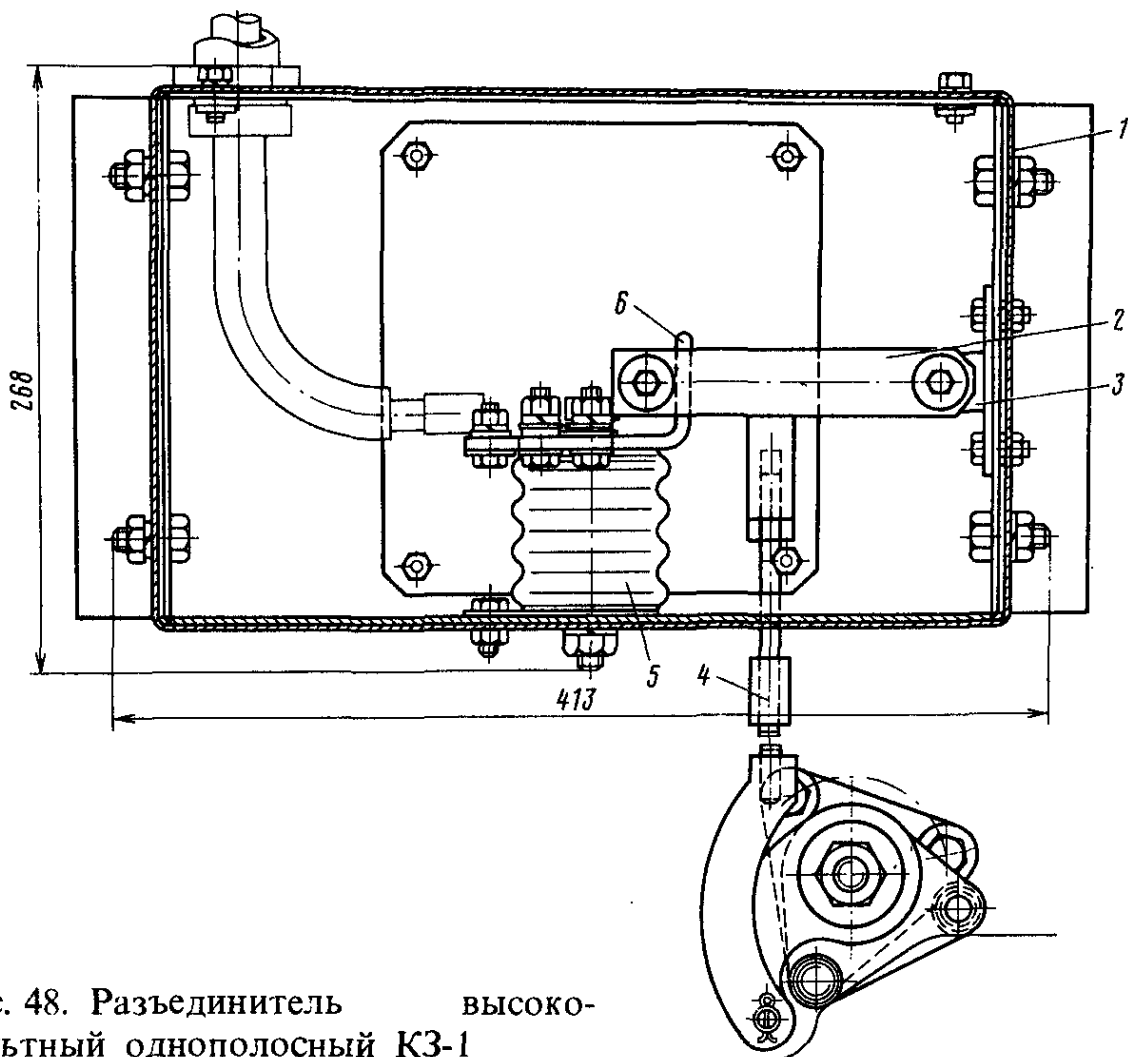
Разъединитель высоковольтный однополюсный КЗ-1
